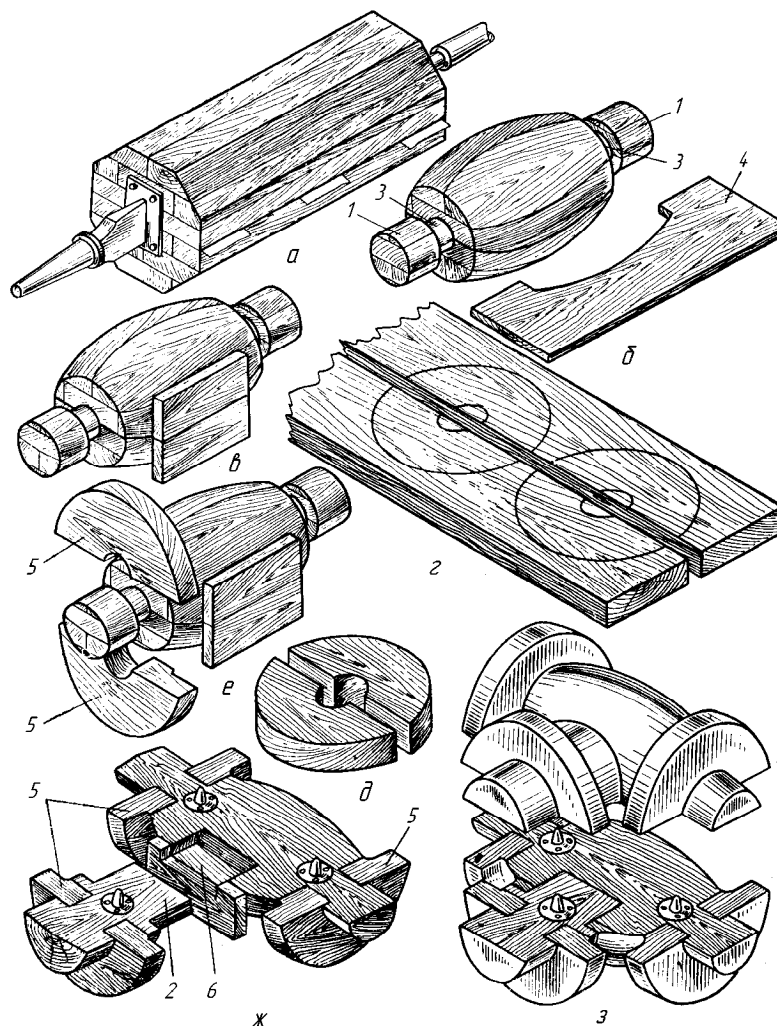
Процесс изготовления модели «Корпуса вентиля»
